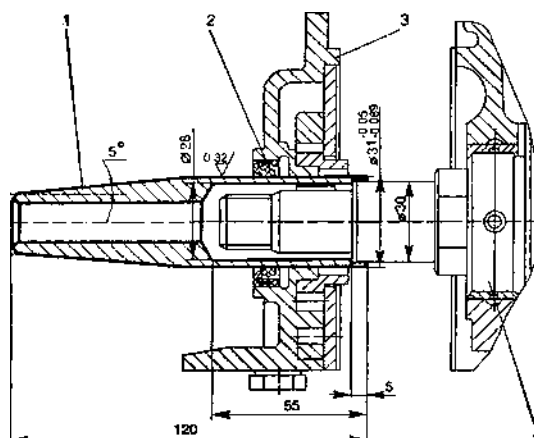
Установка масляного насоса на носок коленчатого вала:
